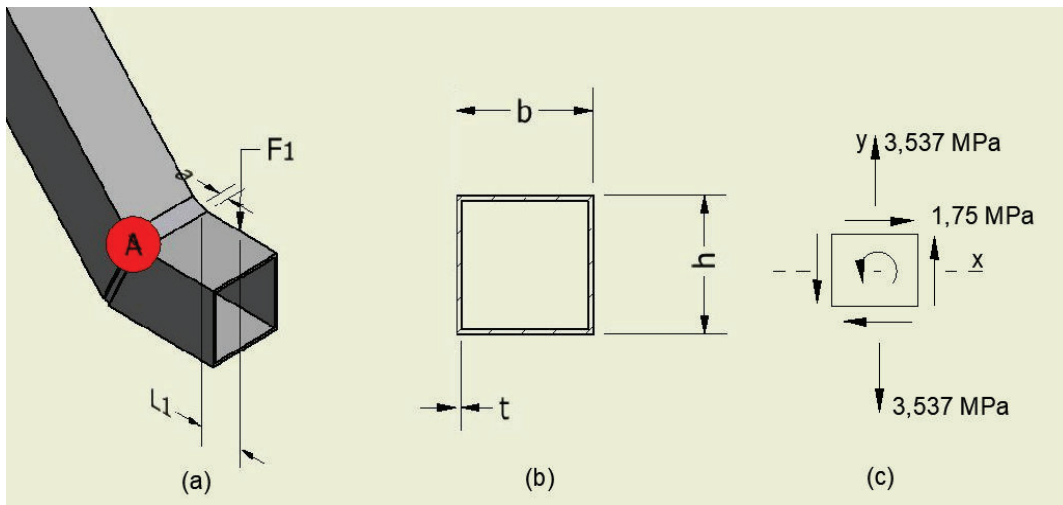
(a) Punto crítico en soldadura (b) Sección transversal del tubo y dimensiones (c) Elemento de esfuerzos en el punto A.
